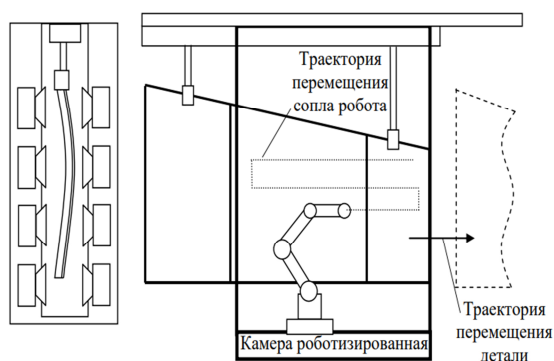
Схема крепления детали на установке МР 20000 проходного типа
